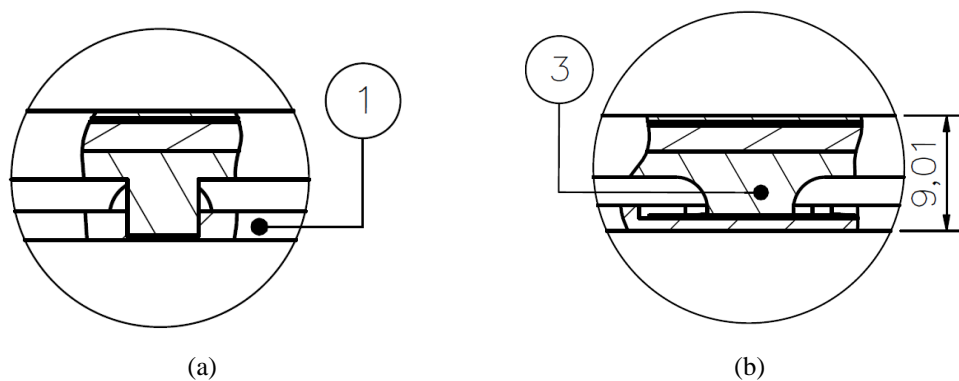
Vistas de detalle de la plantilla: (a) Detalle C y (b) Detalle B.
